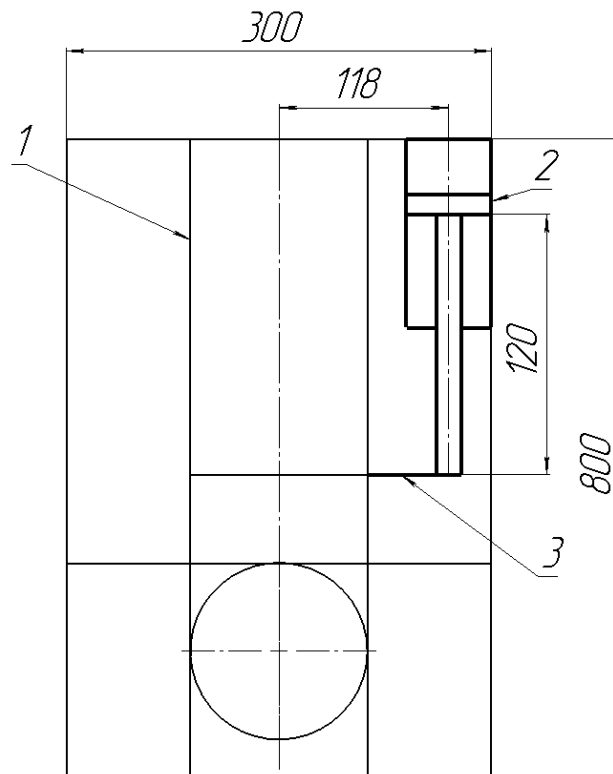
Розрахункова схема встановлення пневмоциліндру, вид зверху: 1 – шліфувальний вузол; 2 – пневмоциліндр; 3 – кронштейн.
